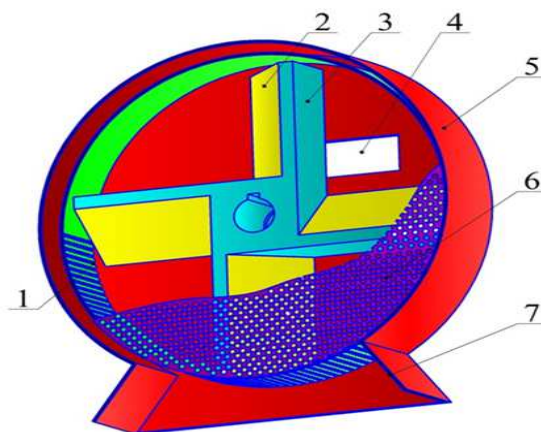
Модель дробилки зерна с жестко закрепленными билами:
